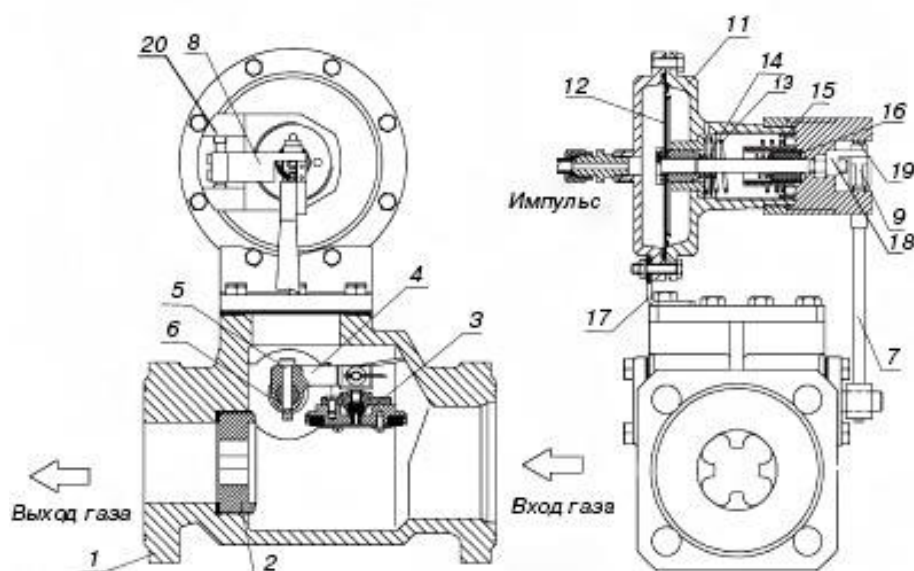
Предохранительный запорный клапан КПЗ-50 [24]
